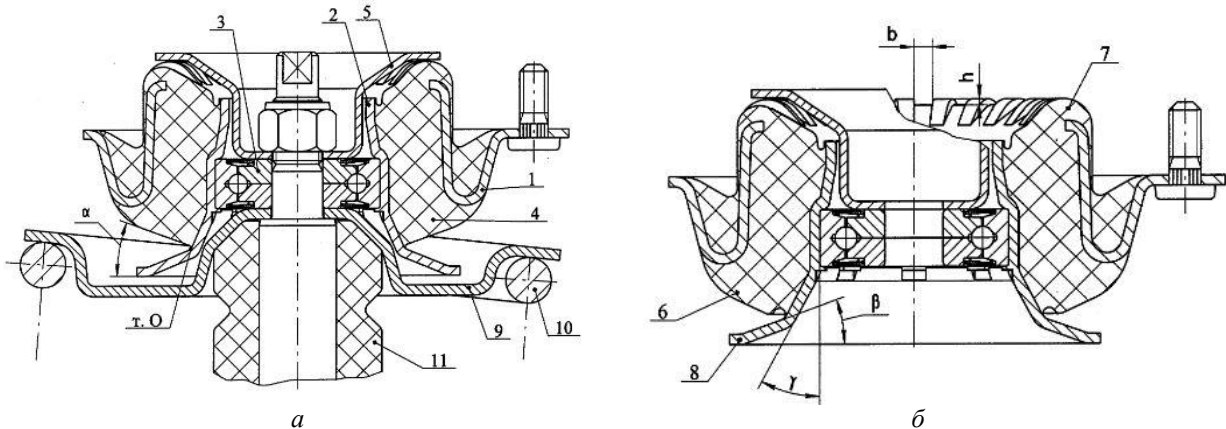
Верхняя опора направляющей пружинной стойки подвески транспортного средства:
